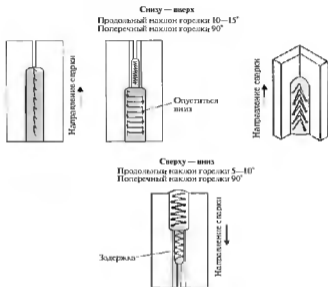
Манипулирование горелкой при сварке в вертикальном положении
